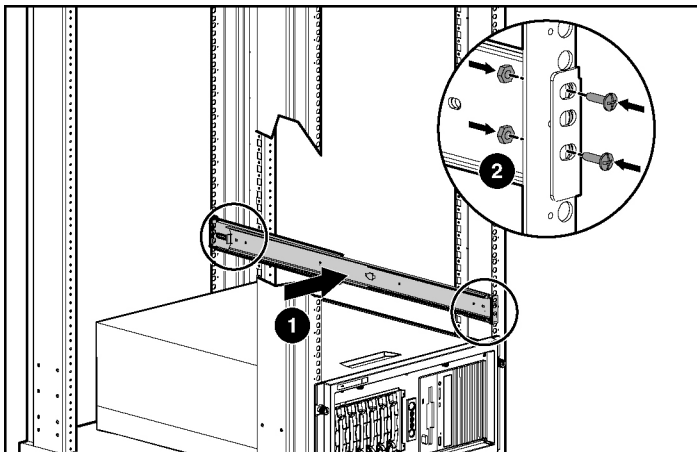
Fixação do conjunto deslizante do suporte do rack com orifícios redondos
